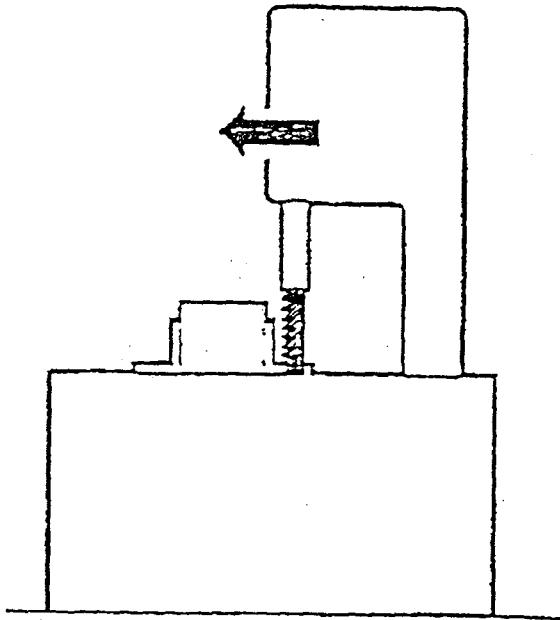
Вертикальний стрічковопиляльний верстат для фронтального різання
